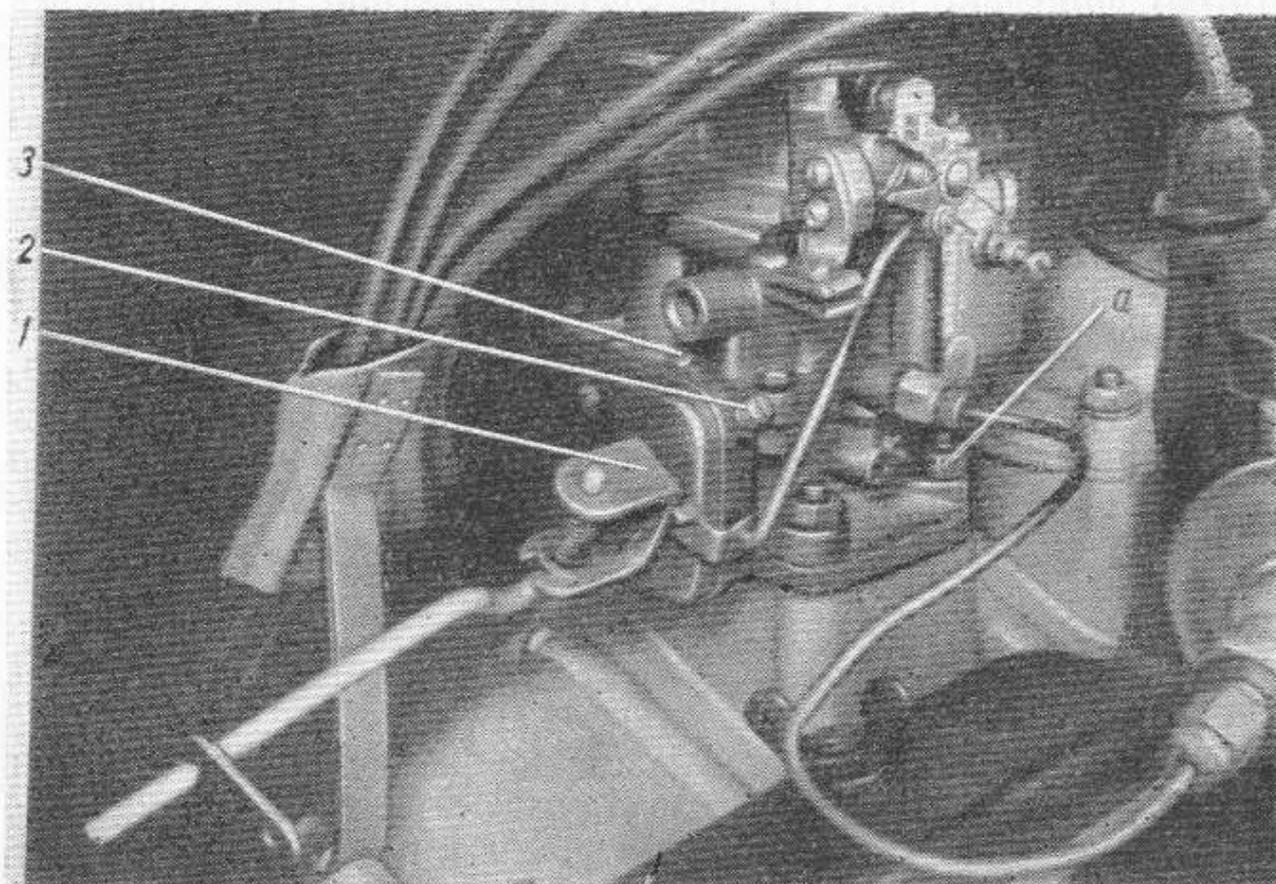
Vergaserschrauben zur Einstellung des Leerlaufgemisches:
